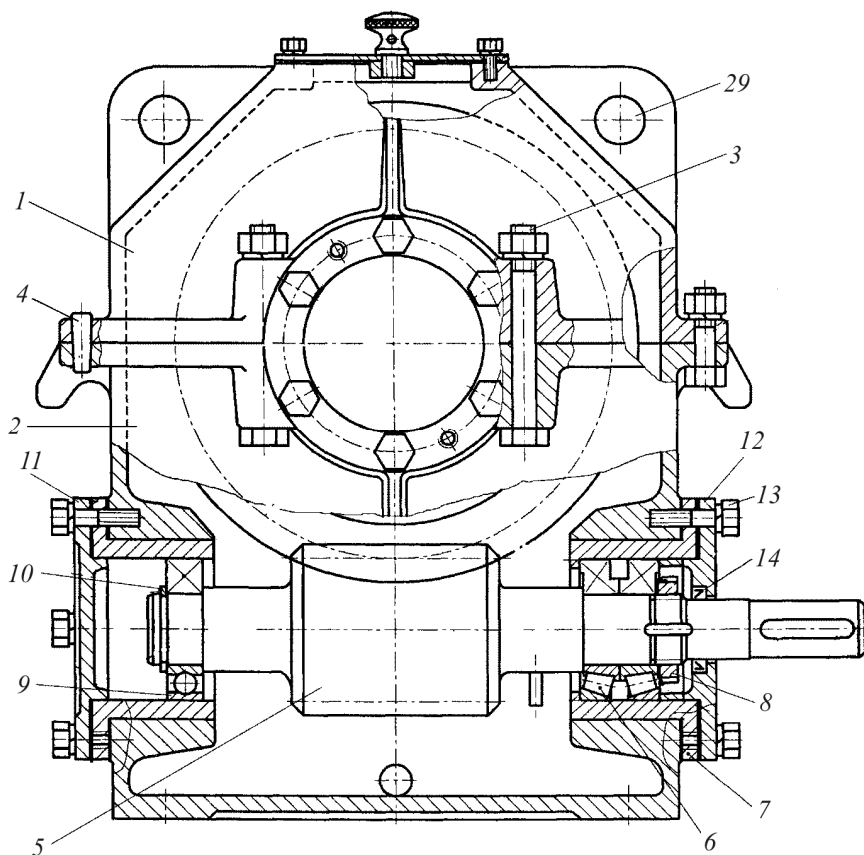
Редуктор червячный одноступенчатый (см. с. 42)
